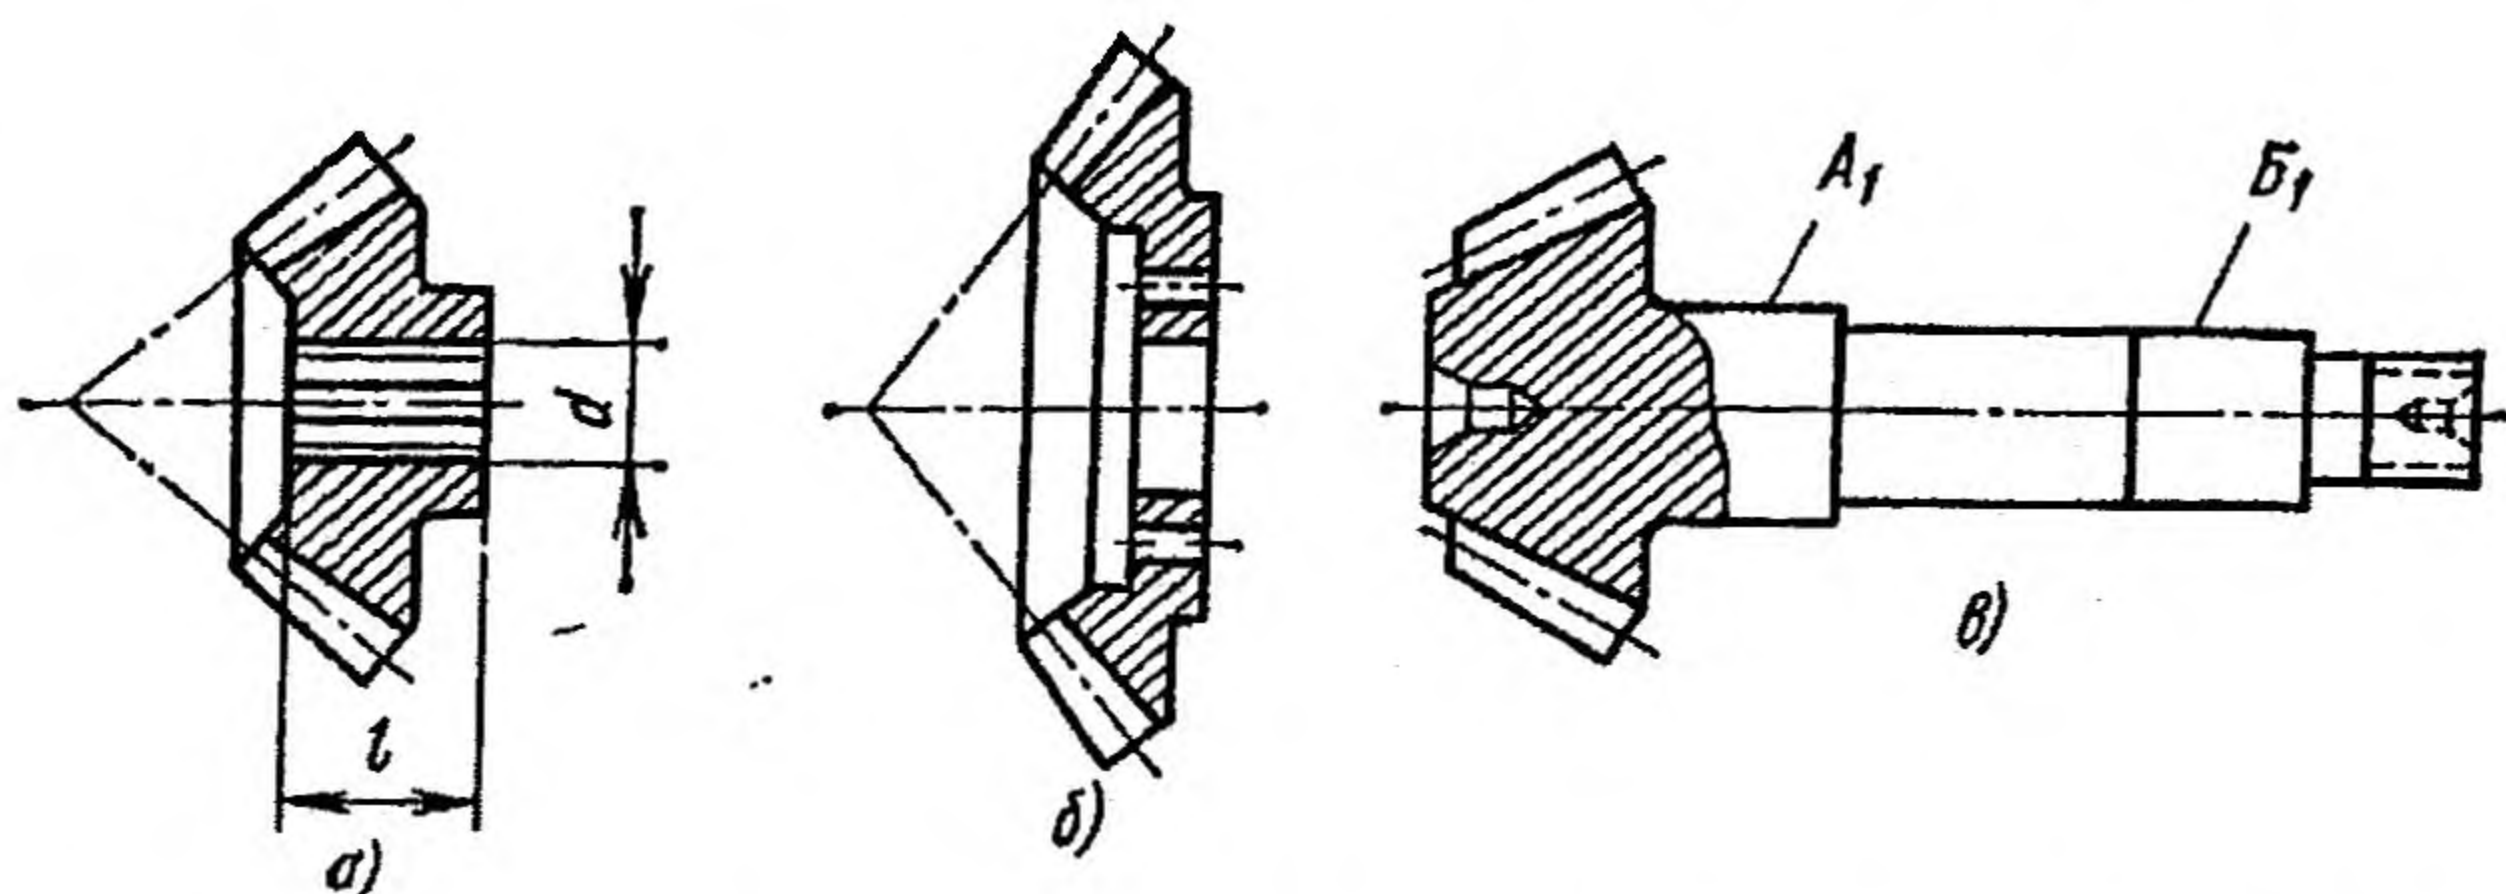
Конструктивные разновидности конических зубчатых колес
